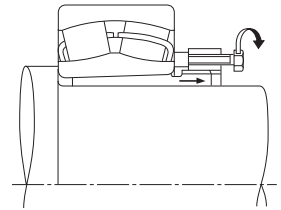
Extracción del Manguito de Desmontaje Utilizando una Tuerca de Desmontaje (2)
